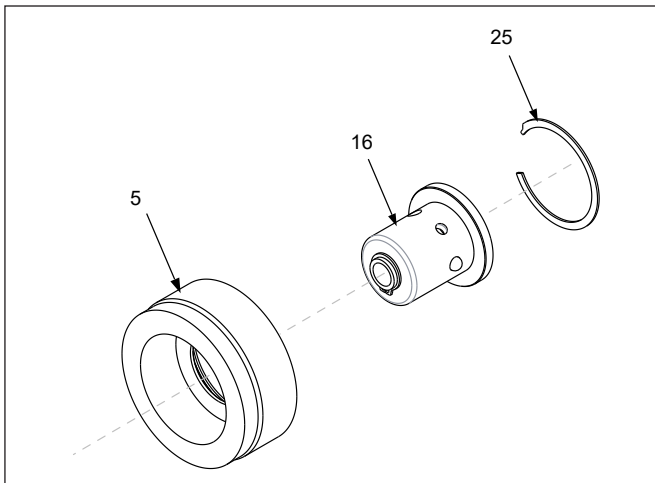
Explosionsansicht Montage der Halterung der Drucktaste
